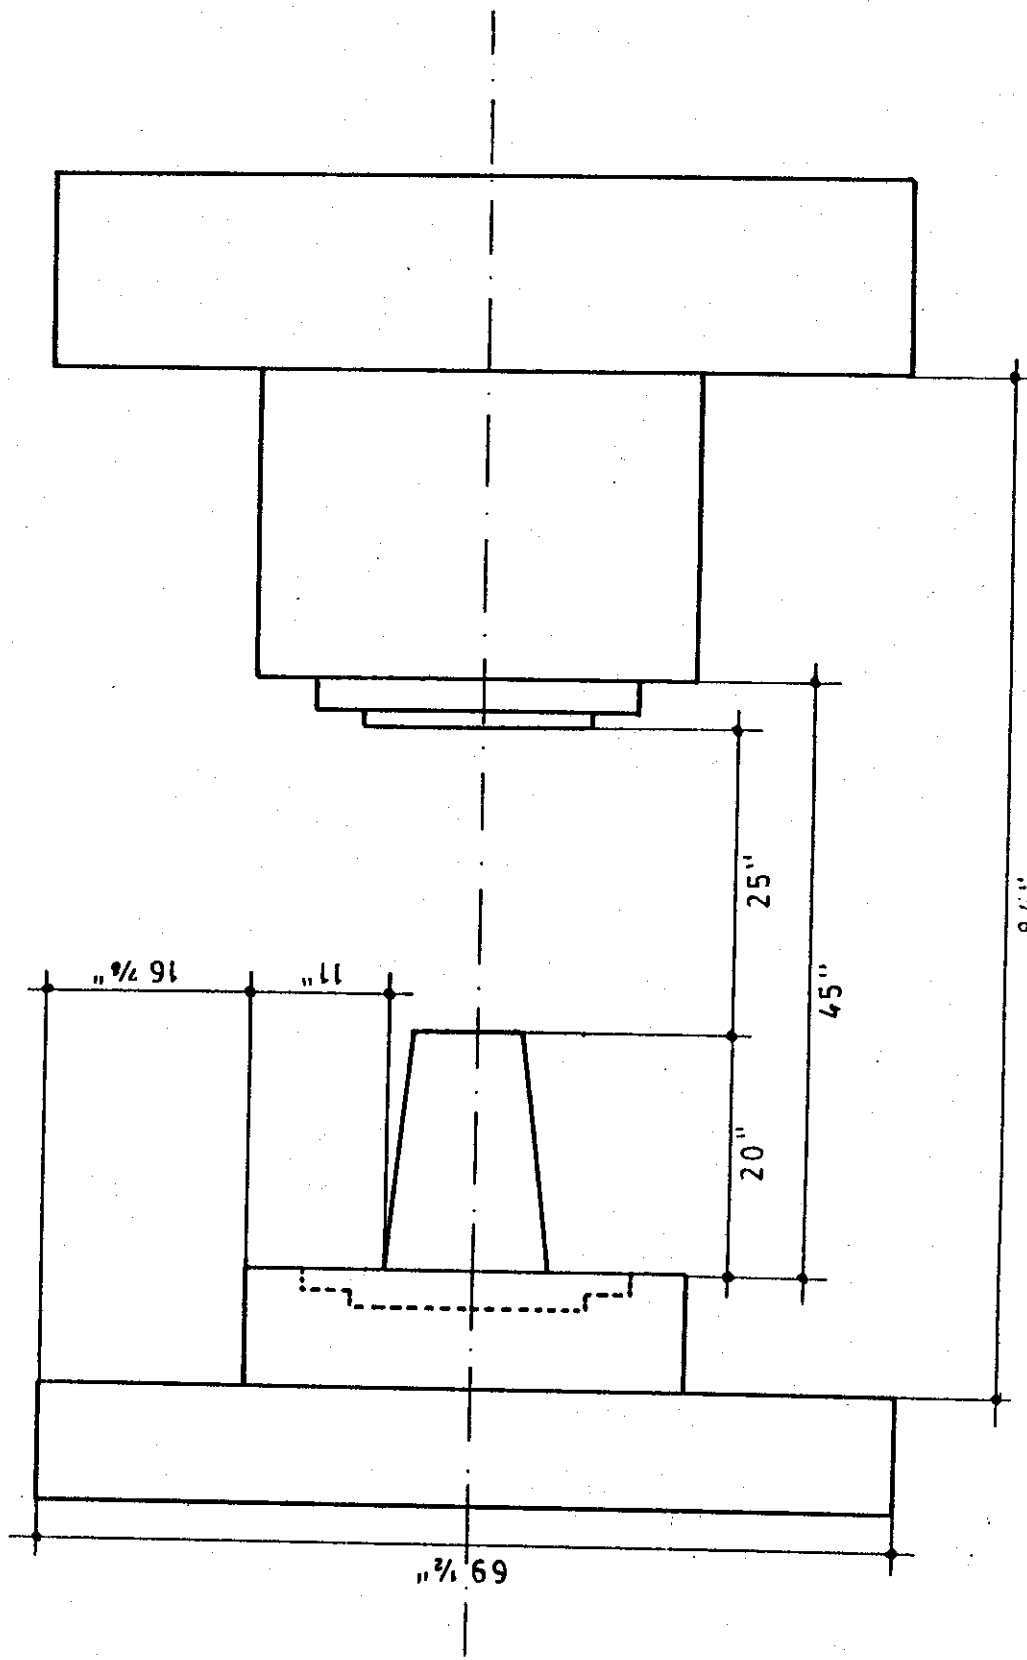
PLANTA DEL MOLDE Y PLATINAS
